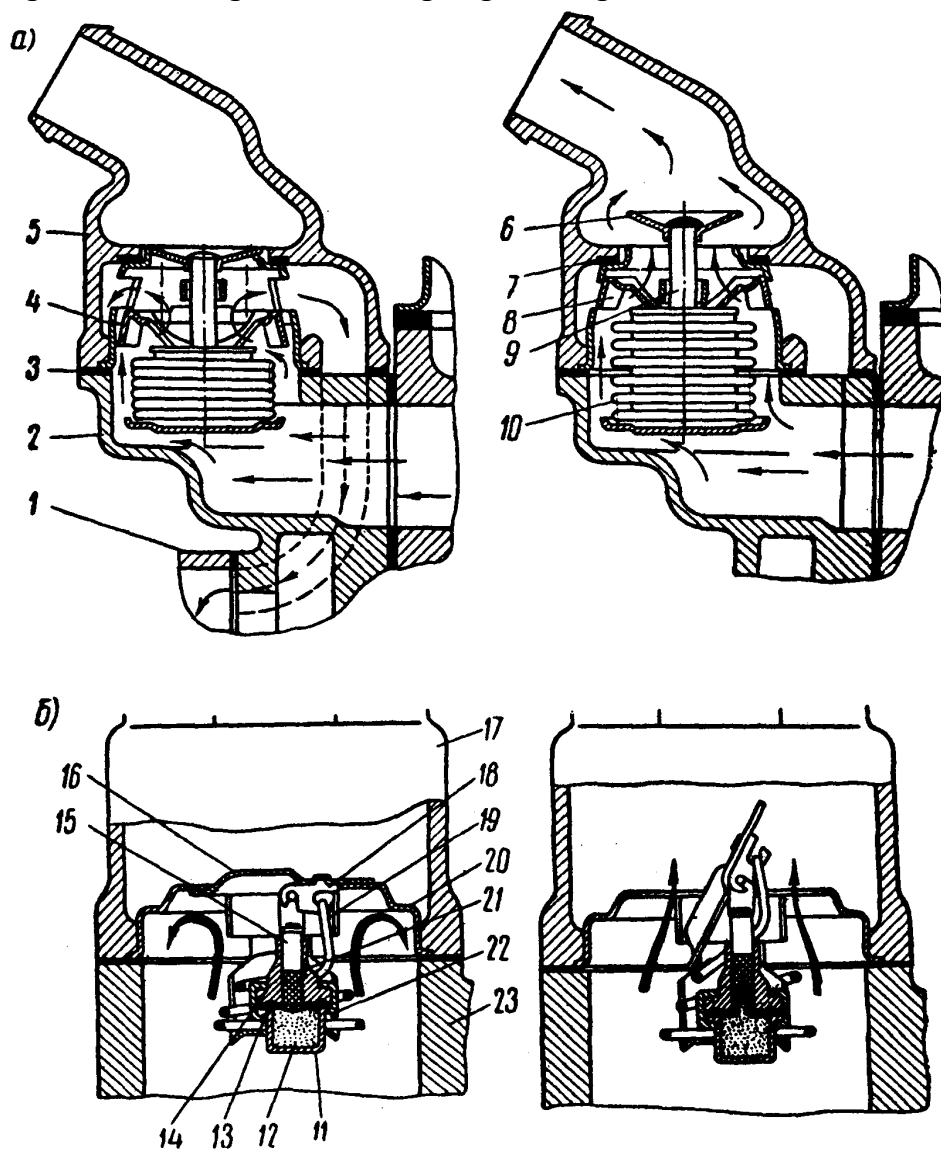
Термостати: а) – рідинний (сильфонний); б) – з твердим наповнювачем і поворотним клапаном: 1, 2 - патрубок; 3, 7 - прокладки; 4 - корпус термостата; 5 - патрубок вихідний; 6 - основний клапан; 8 - перепускний клапан; 9 - стержень сильфона; 10 - сильфон; 11 - мідний балон; 12 - активна маса; 13 - гумова мембрана; 14 - направляюча; 15 - шток; 16 - заслінка; 17, 23 - патрубки; 18 - коромисло; 19 - пружина; 20 - отвір; 21 - гумовий буфер; 22 - скоба
